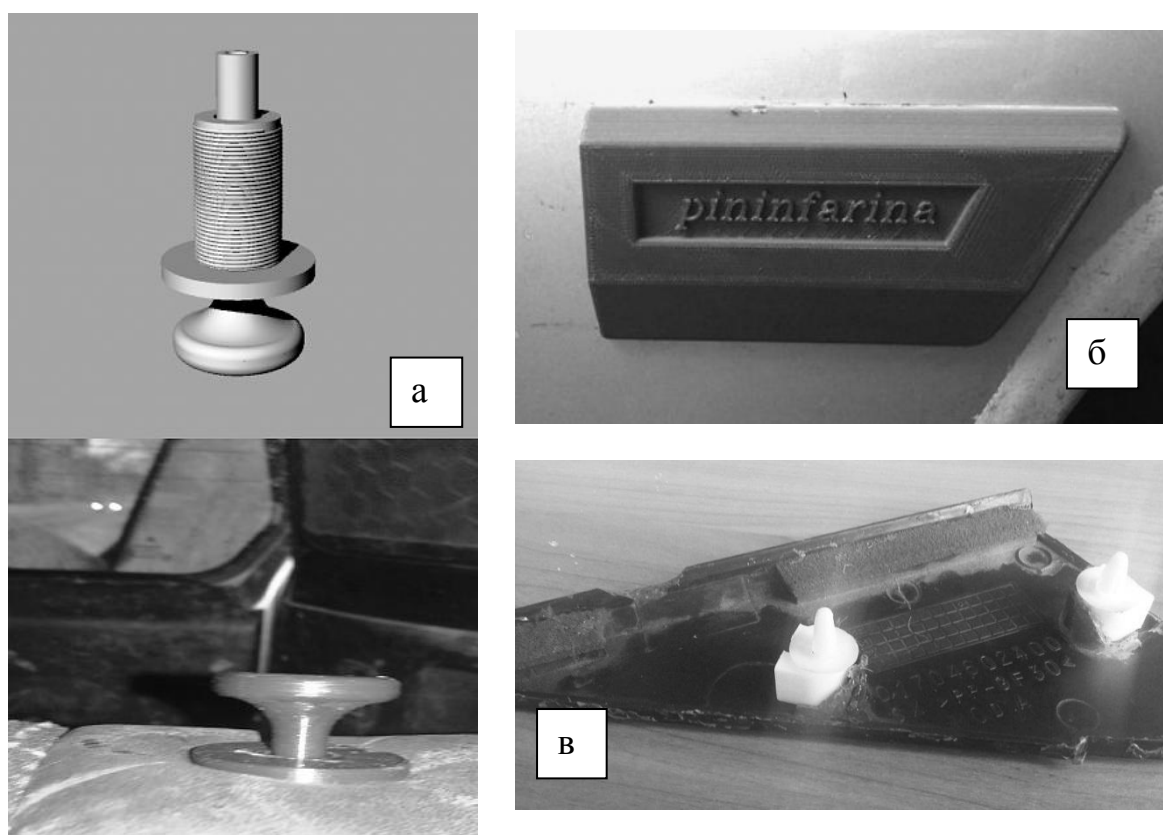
Ремонт пластмассовых деталей автомобиля Mitsubishi Pajero Pinin с помощью 3D-принтера: а – ручка механизма раскладывания заднего сиденья (пластик PLA PrintProduct; сверху – общий вид ручки, снизу – ручка, вмонтированная в сиденье); б – молдинг переднего крыла (пластик ABS 3D Lines); в – ремонтные вставки для крышки зеркала (пластик PLA Esun)
